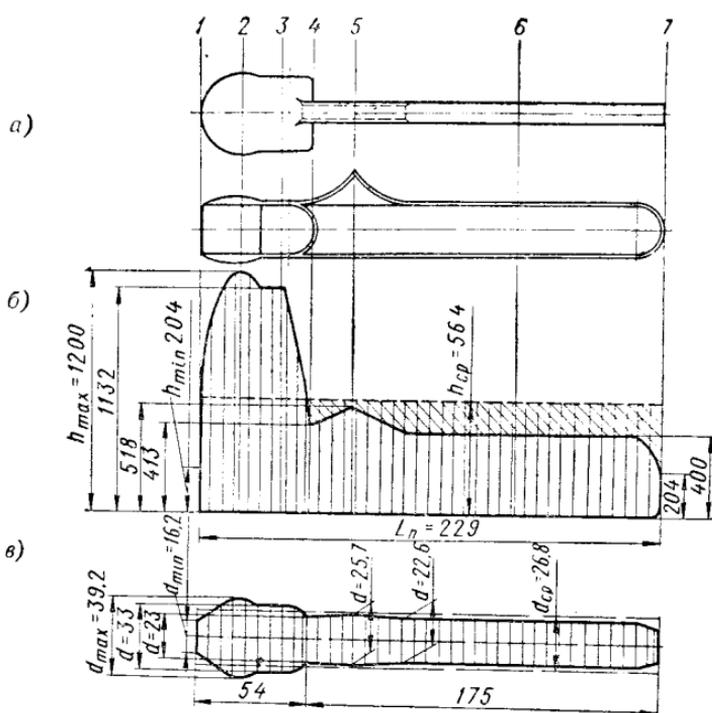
Развертка горячей поковки (а), эиоры сечений (б) и расчетная заготовка (в) рычага тормозного крана (1—7 — номера сечений)
